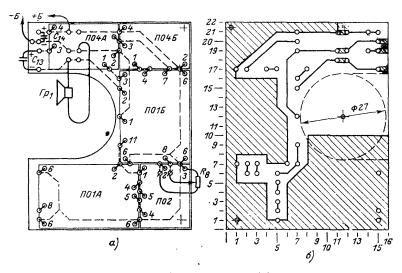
Монтажный эскиз сборочной платы (a) и рисунок проводников (b).
